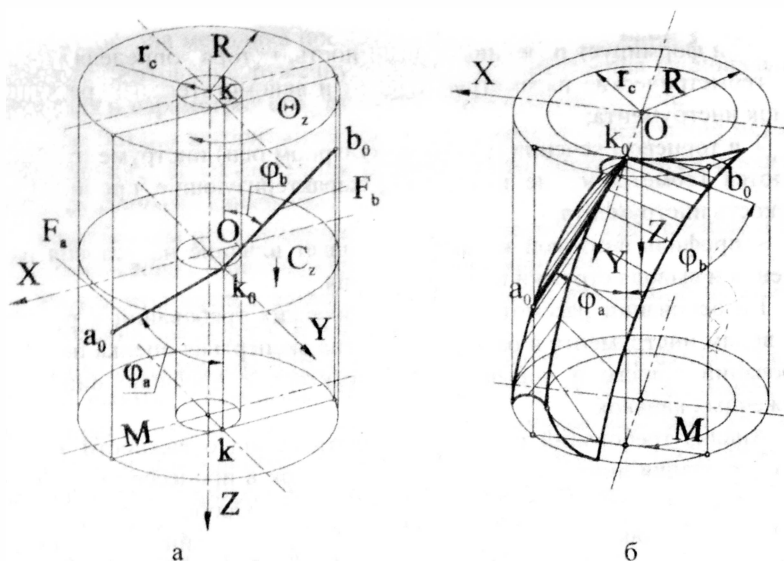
Принципиальная схема образования линейчатой винтовой поверхности стружечной канавки инструмента
